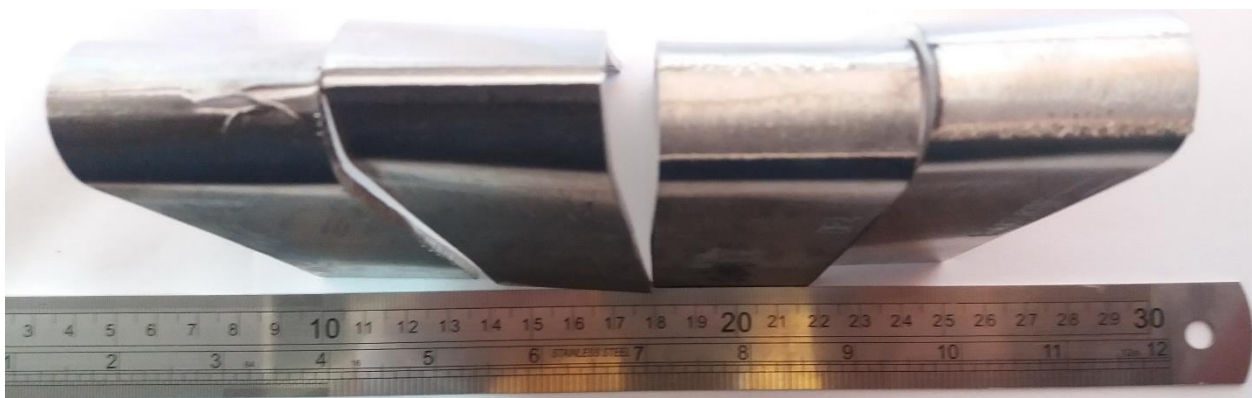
Dobramentos de face e raiz para velocidade de soldagem de 80 mm/min. Fonte: os autores, 2016.
